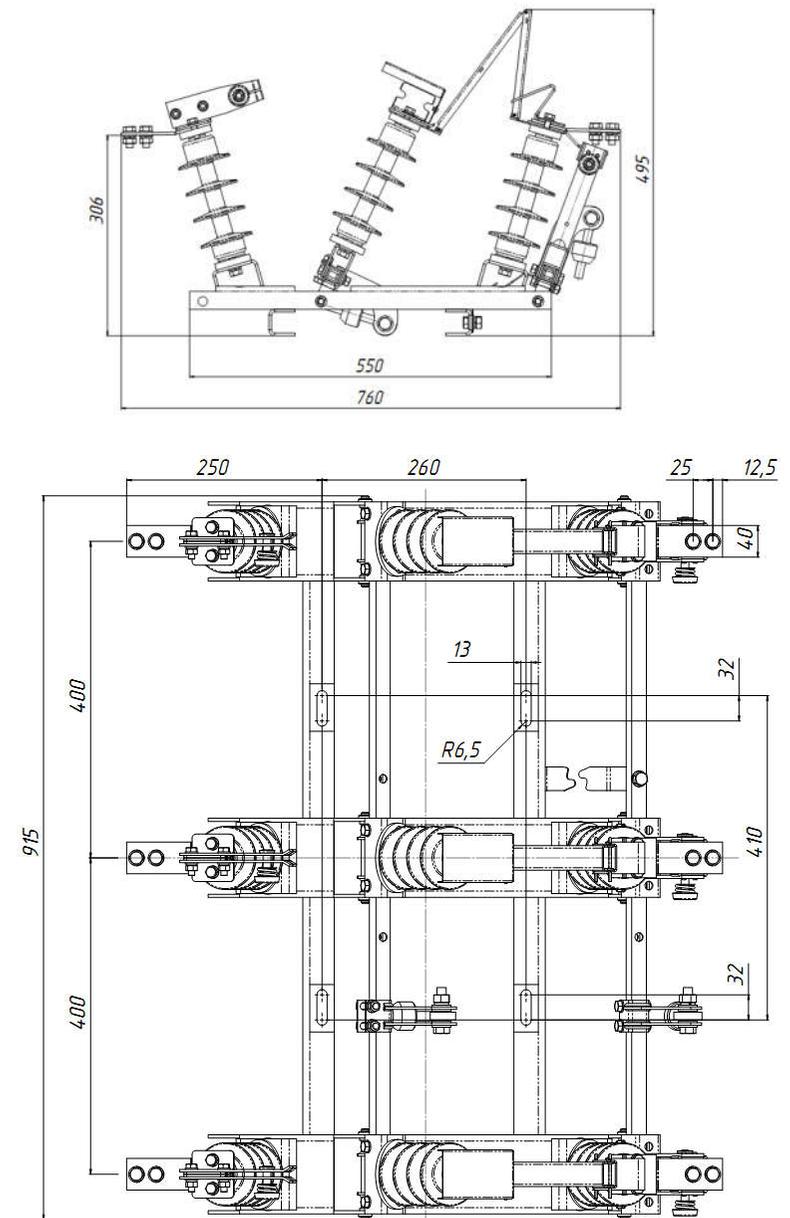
Б Разъединитель РЛК-16-II-10/400 –УХЛ1
